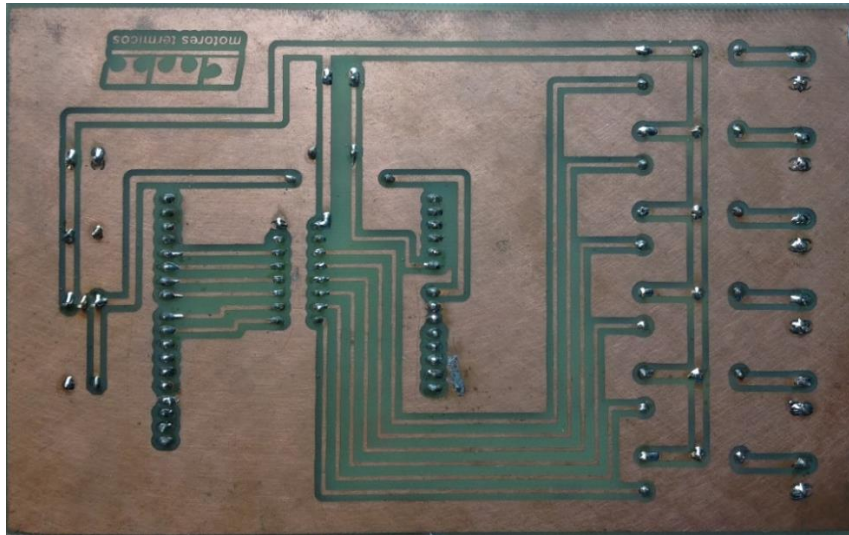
B Parte Inferior del Circuito Integrado Soldado
